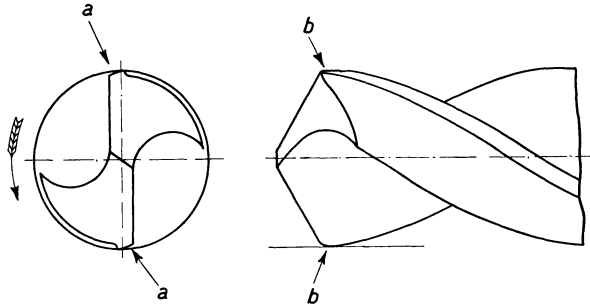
Fehler am Spiralbohrer beim Glätten mit dem Ölstein.
